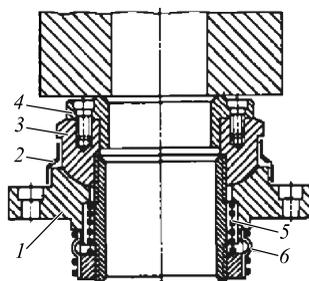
Приспособление для протягивания отверстия в заготовках с обработанным торцом
